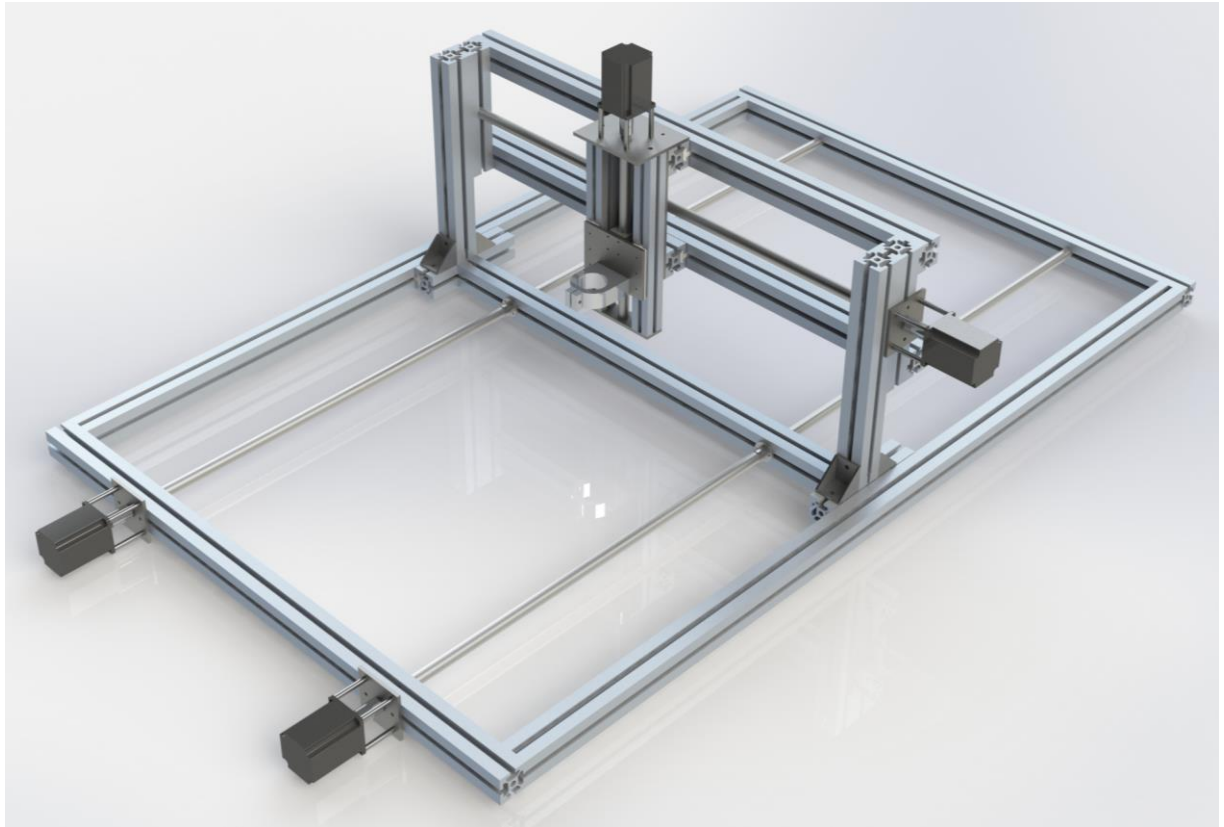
Representación en SolidWorks del diseño final de la fresadora CNC
